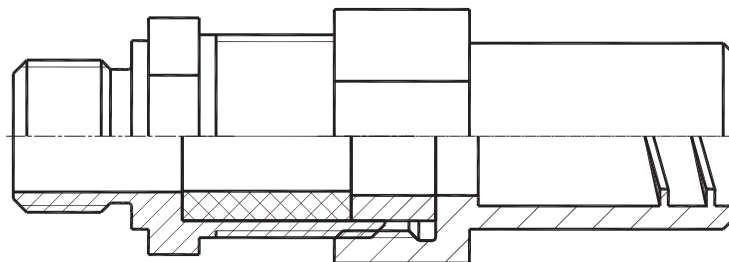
Конструкция ВКВ для монтажа кабеля в металлорукаве.
